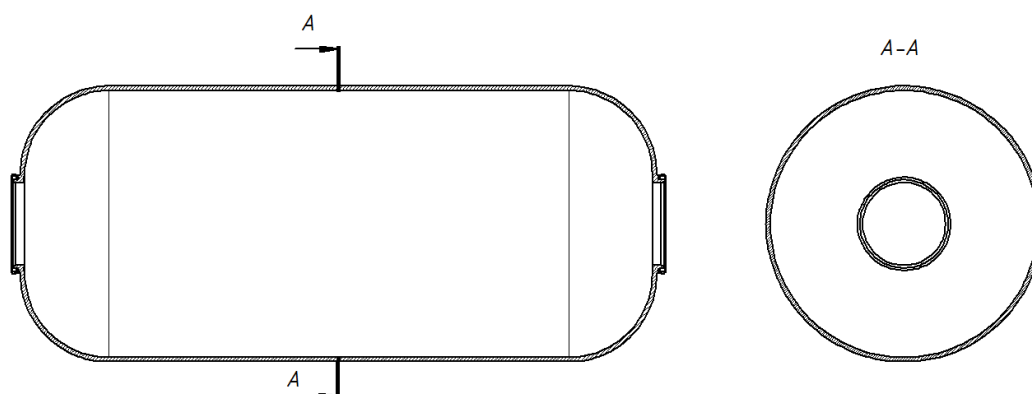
Конструктивная схема цельнометаллической оправки
